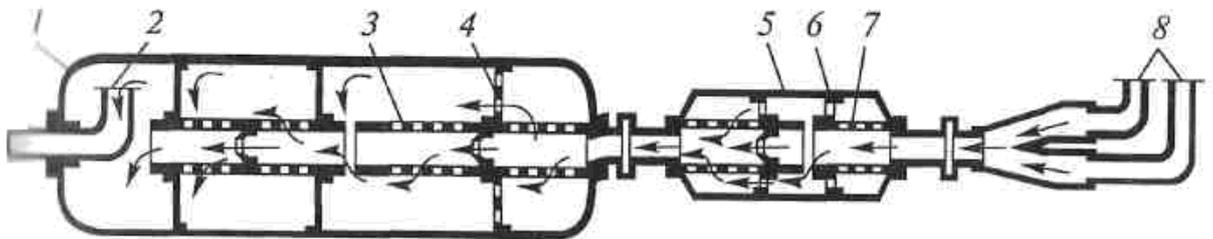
Глушители: 1 - основной глушитель; 2, 3, 7, 8 — трубы; 4, 6 — перегородки; 5 — дополнительный глушитель
